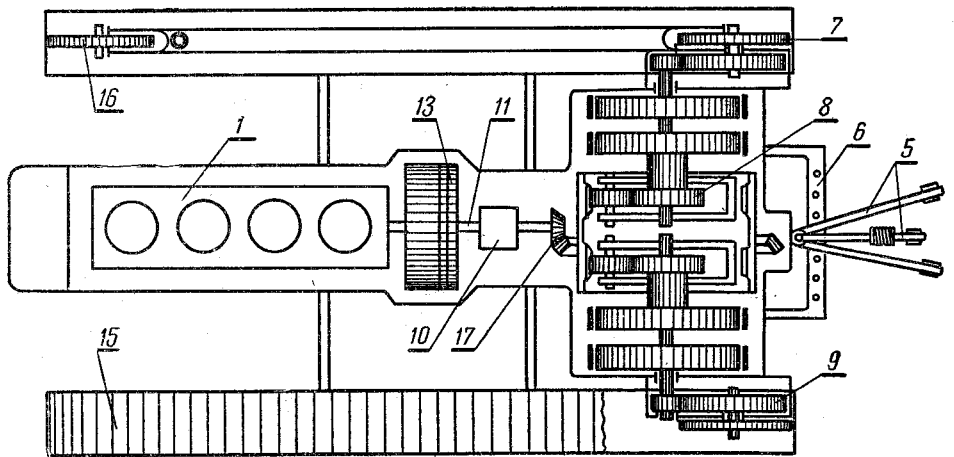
, А. Схема расположения основных механизмов гусеничного трактора ДТ-75:
